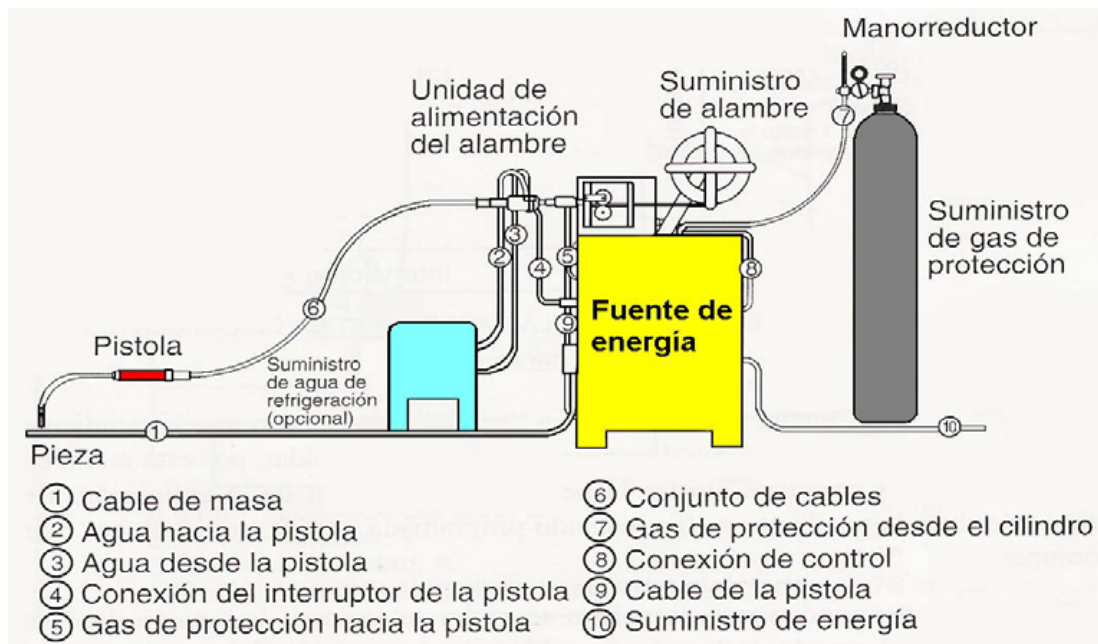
Partes y Componentes de un equipo de soldadura GMAW.
